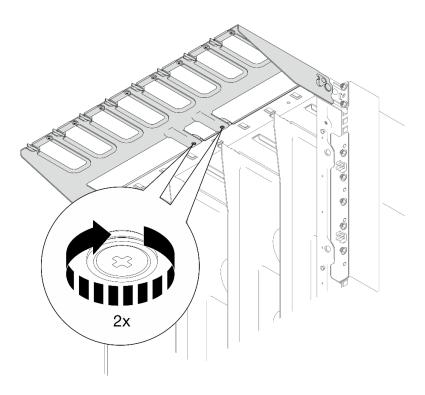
Instalación de dos tornillos desde debajo de la abrazadera de soporte frontal superior
